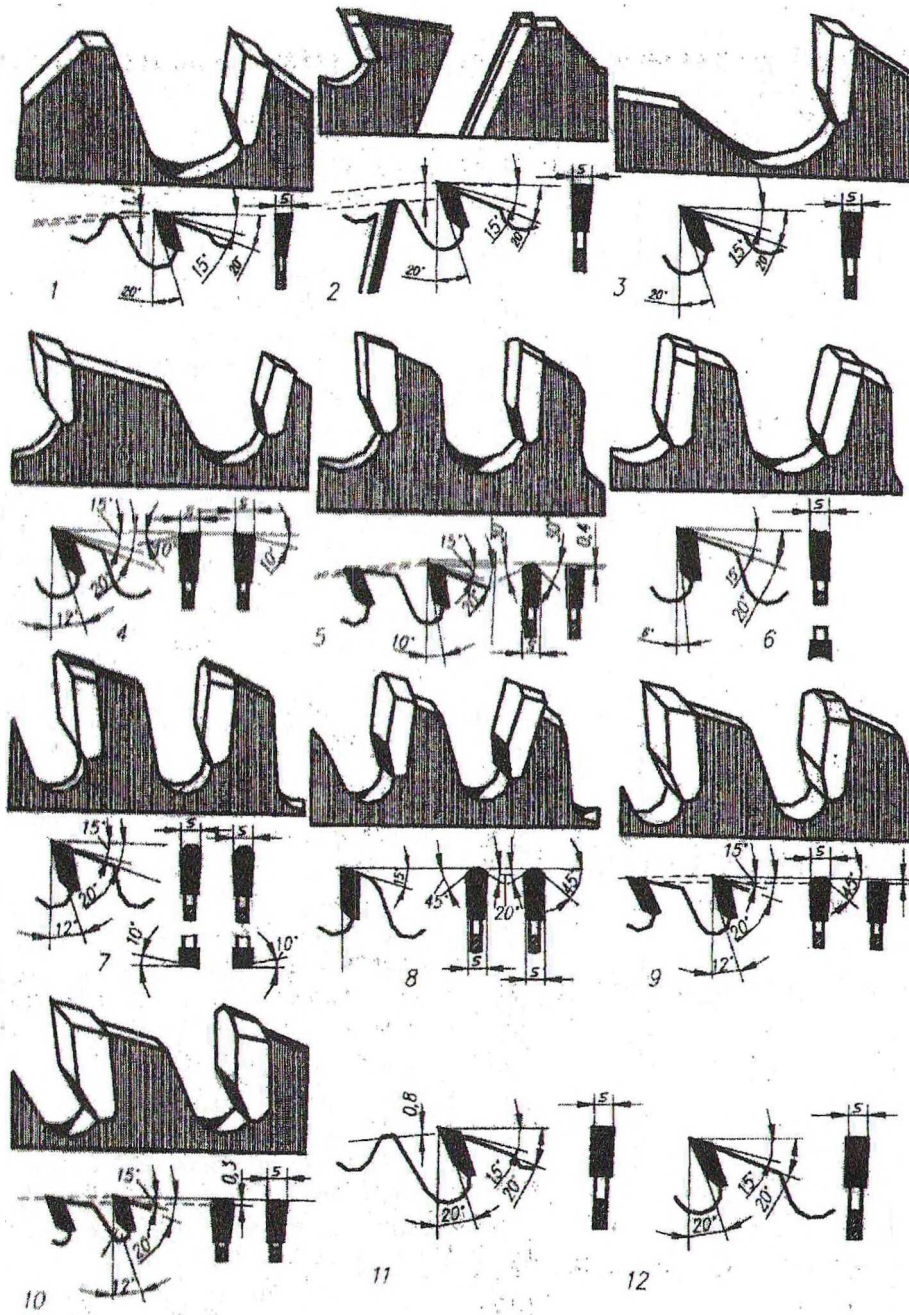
Профили зубьев импортных пил с пластинками из твердого сплава
